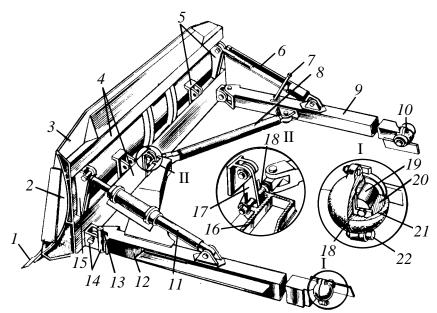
Рабочее оборудование бульдозера с неповоротным отвалом и гидроперекосом:
